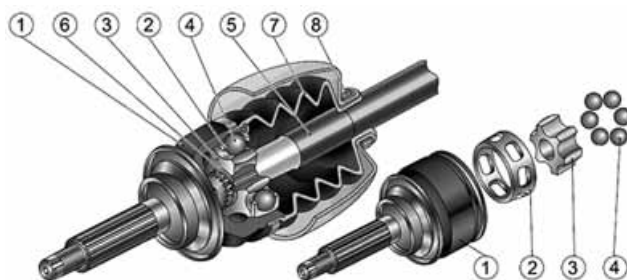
Шарнир равных угловых скоростей: 1 – корпус с наружной обоймой; 2 – сепаратор; 3 – внутренняя обойма; 4 – шарики; 5 – вал привода; 6 – стопорное кольцо; 7 – чехол гофрированный; 8 – хомуты чехла.
